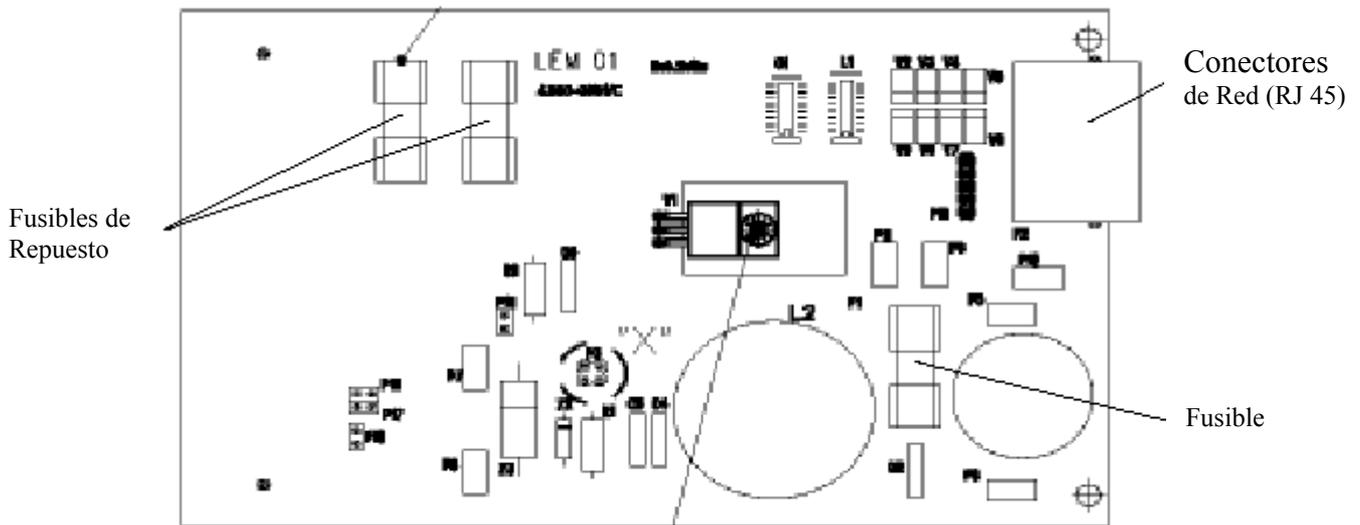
a: Fusibles PCB LEM 01 (lateral componentes)
